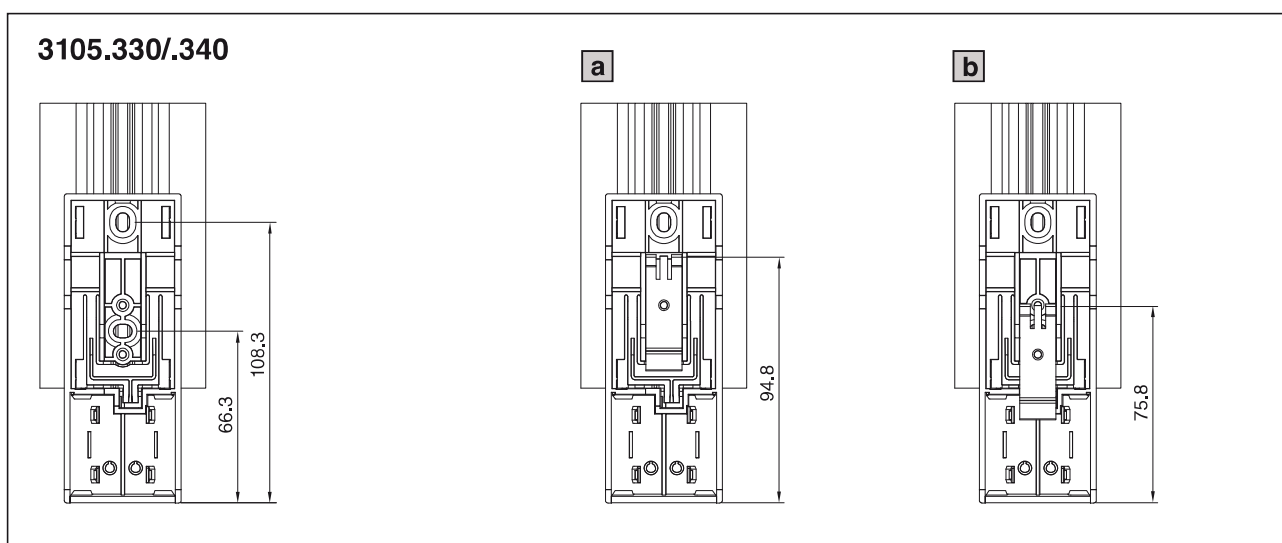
Fixation sur plaque de montage / Possibilités de fixation sur rail porteur
